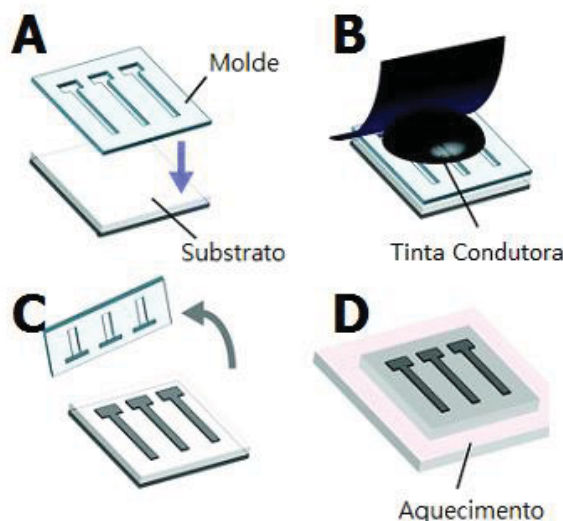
Representação esquemática da fabricação de eletrodos impressos comumente utilizada. (A) Molde é posicionado sobre a superfície do substrato; (B) Tinta condutora é colocada sobre o molde, sendo espalhada com o auxílio de um stencil ou rolo; (C) Após a secagem da tinta, o molde é retirado, sendo obtidos os eletrodos; (D) Finalmente, realiza-se uma etapa de cura da tinta impressa sobre o substrato. FONTE: (Adaptado) Godino, *et al.* [64].
